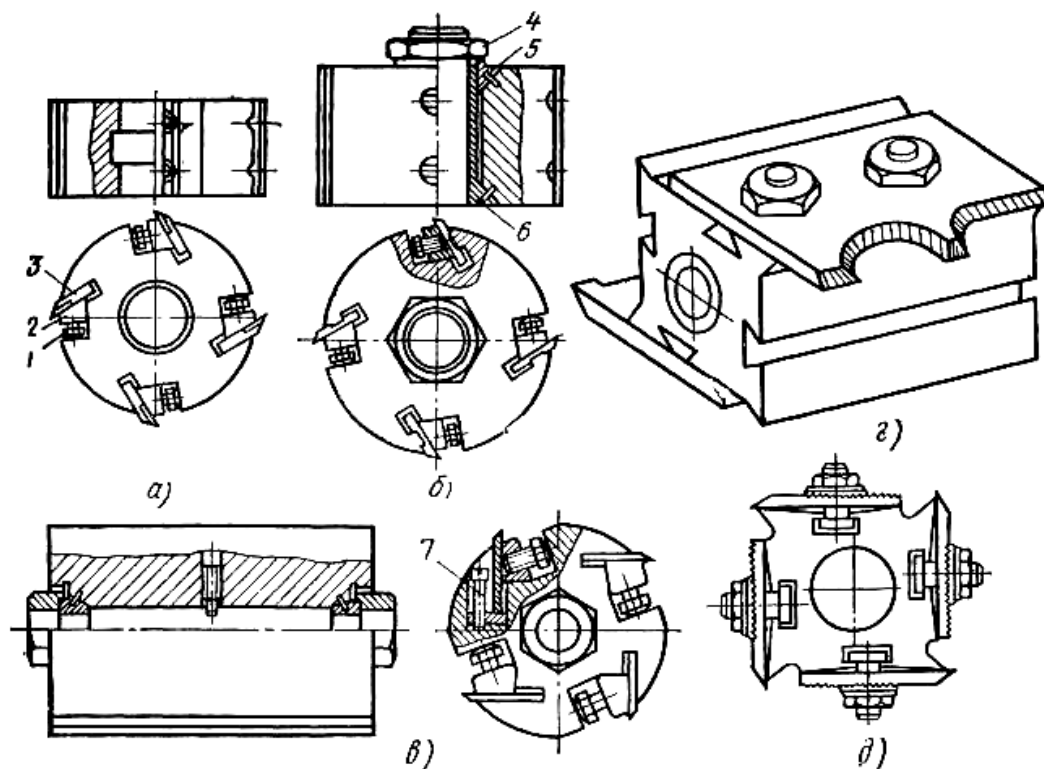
Сборные фрезы к четырехстороннему продольно-фрезерному станку:
